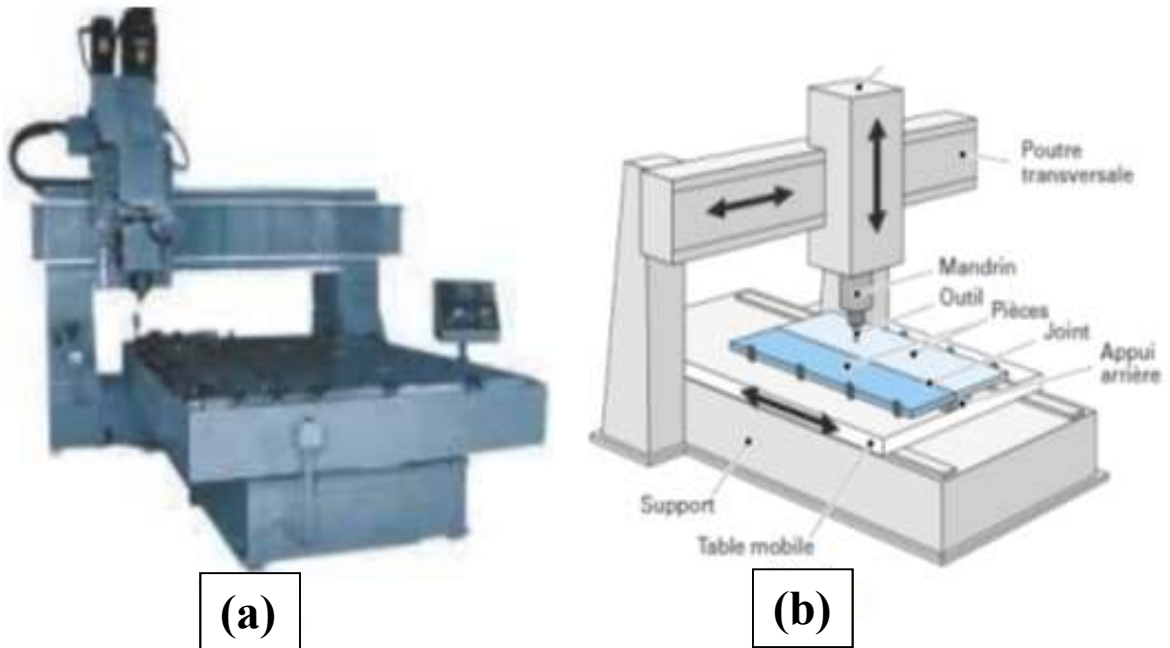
a) Machine réel de FSW. b) Schéma de machine FSW [10].
